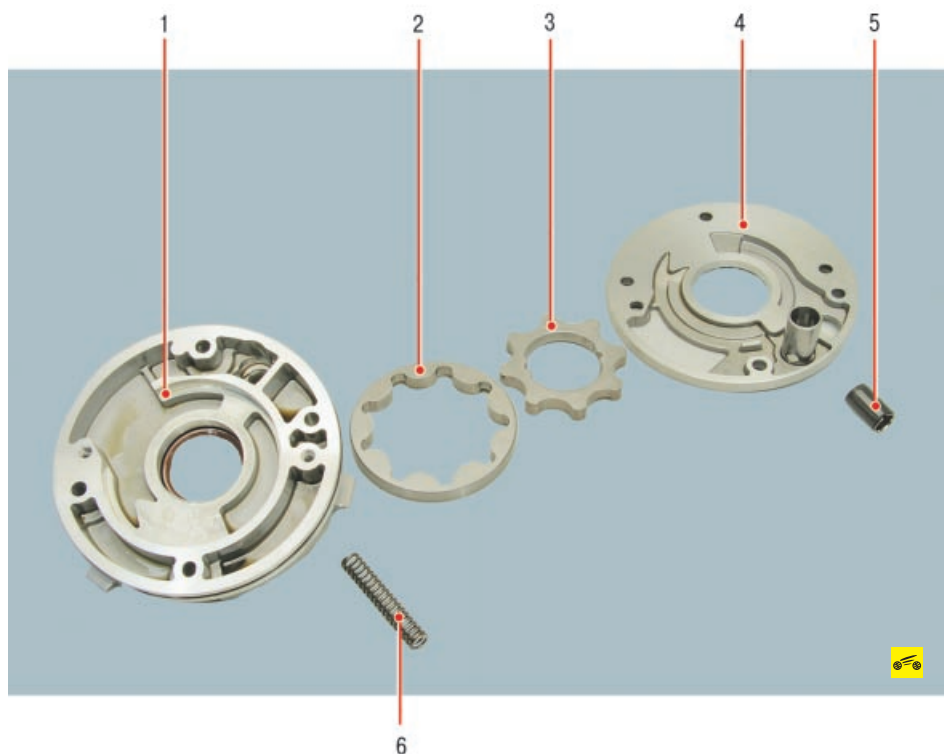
Детали масляного насоса: 1 – корпус насоса; 2 – ведомая шестерня; 3 – ведущая шестерня; 4 – крышка корпуса; 5 – плунжер; 6 – пружина редукционного клапана
